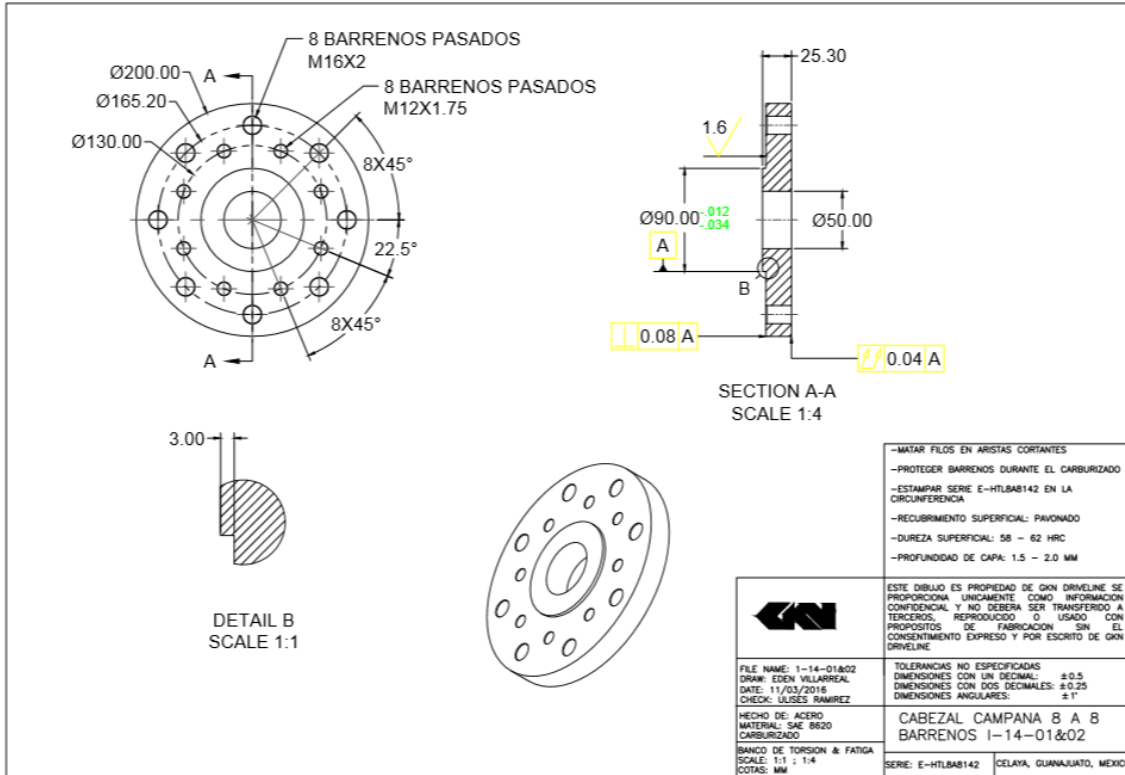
Plano De La Propuesta Del I-14-01&-02
